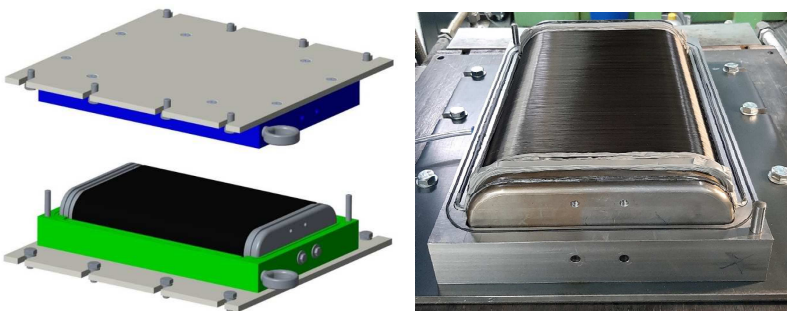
Links: CAD-Zeichnung des Wickel-RTM-Werkzeugs; Rechts: Bewickelter Kern in unterer RTM-Werkzeughälfte
